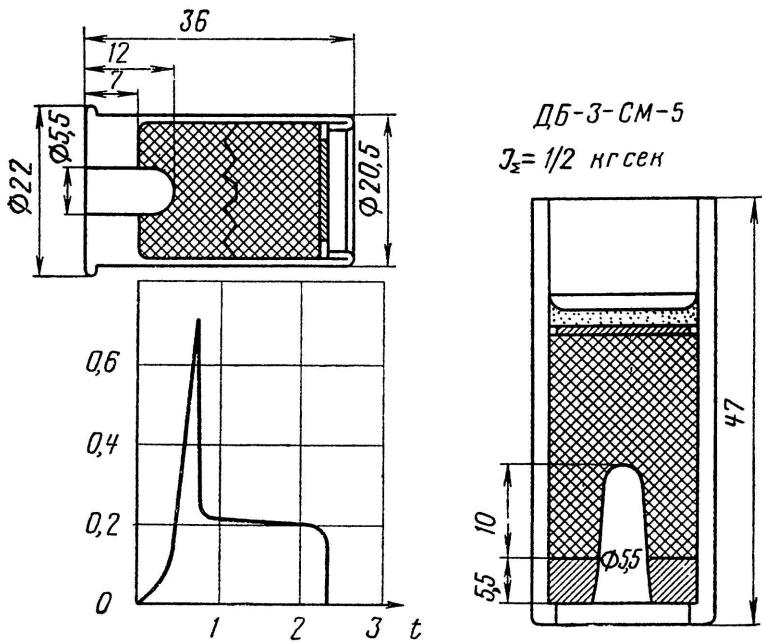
Модельный ракетный двигатель ДБ-3-СМ-5
